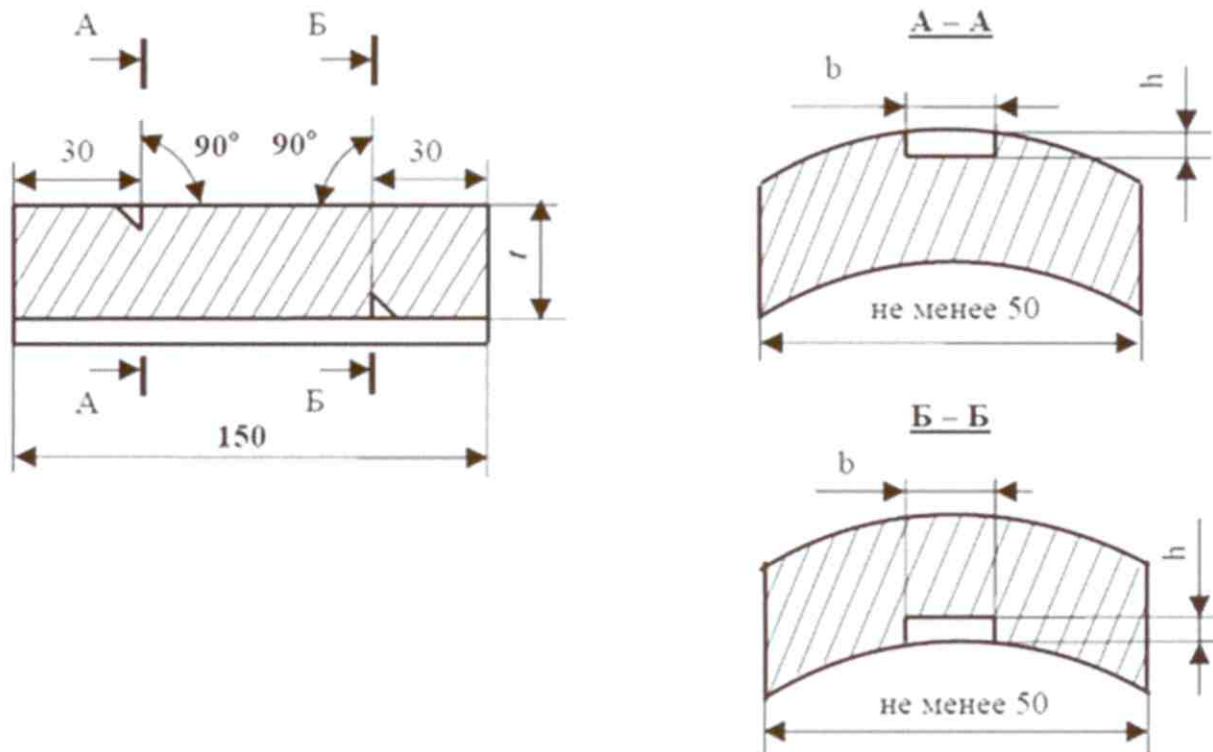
Чертеж калибровочного образца для настройки браковочного уровня
